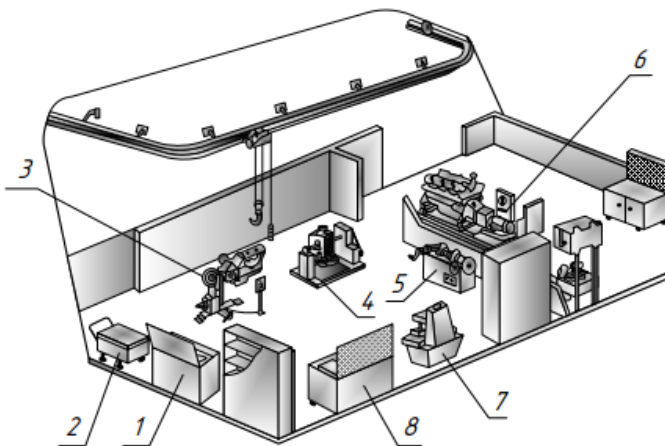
Участок ремонта двигателей: 1 – верстак слесарный с приспособлением для разборки, сборки регулирования муфт сцепления; 2 – ванна моечная передвижная; 3 – стенд для разборки и сборки двигателей; 4 – стенд для разборки и сборки двигателей типа; установка для шлифования фасок клапанов; 6 – стенд обкаточно-тормозной; 7 – стенд для притирки клапанов; 8 – верстак слесарный с приспособлением для шлифования клапанных гнезд
